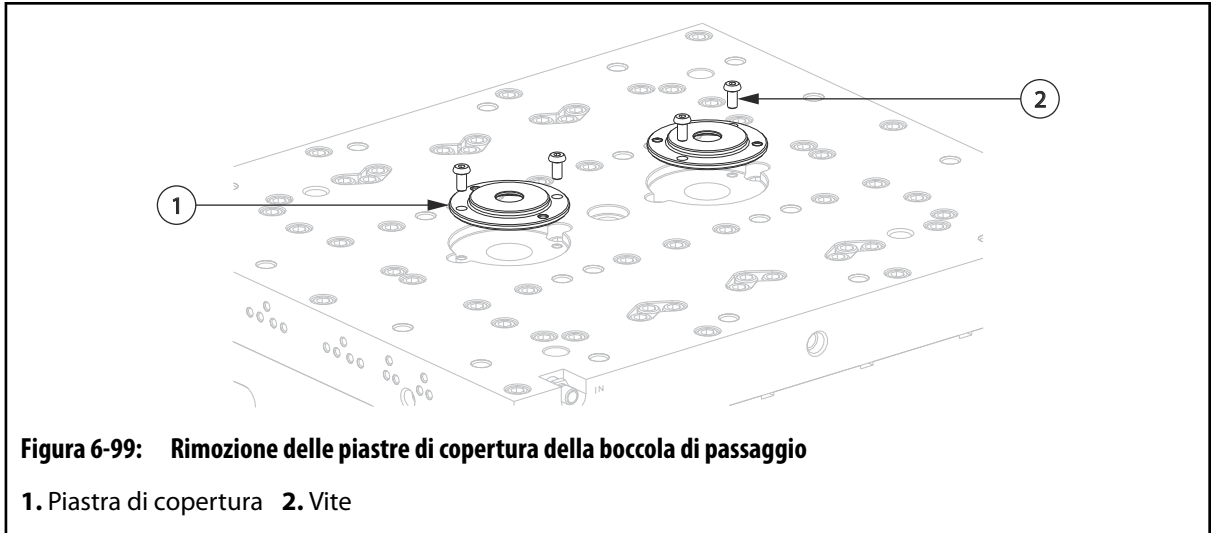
Rimozione delle piastre di copertura della boccola di passaggio
